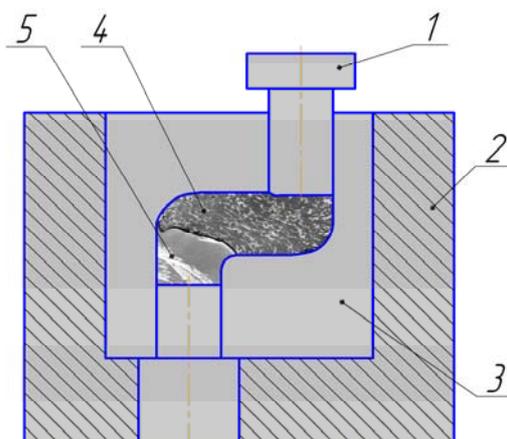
Оснастка для РКУ прессования брикета: 1- пуансон; 2- контейнер; 3- матрица; 4- брикет; 5- подпор.
